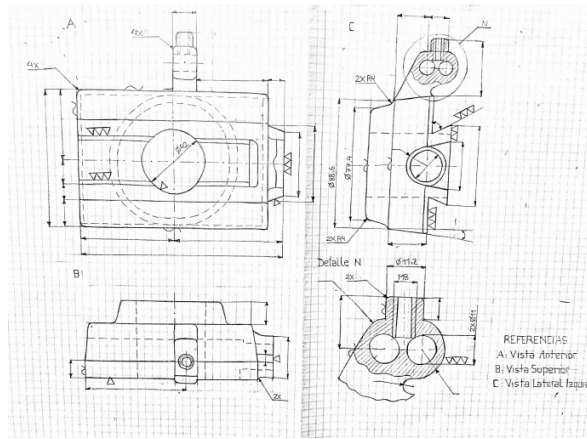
Dibujo de despiece de la pieza denominada cuerpo.
